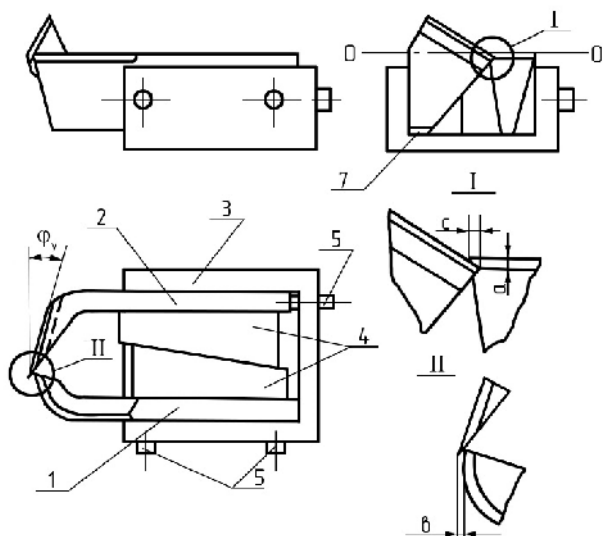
Конструкция резцовой головки с черновым и чистовым резцами
